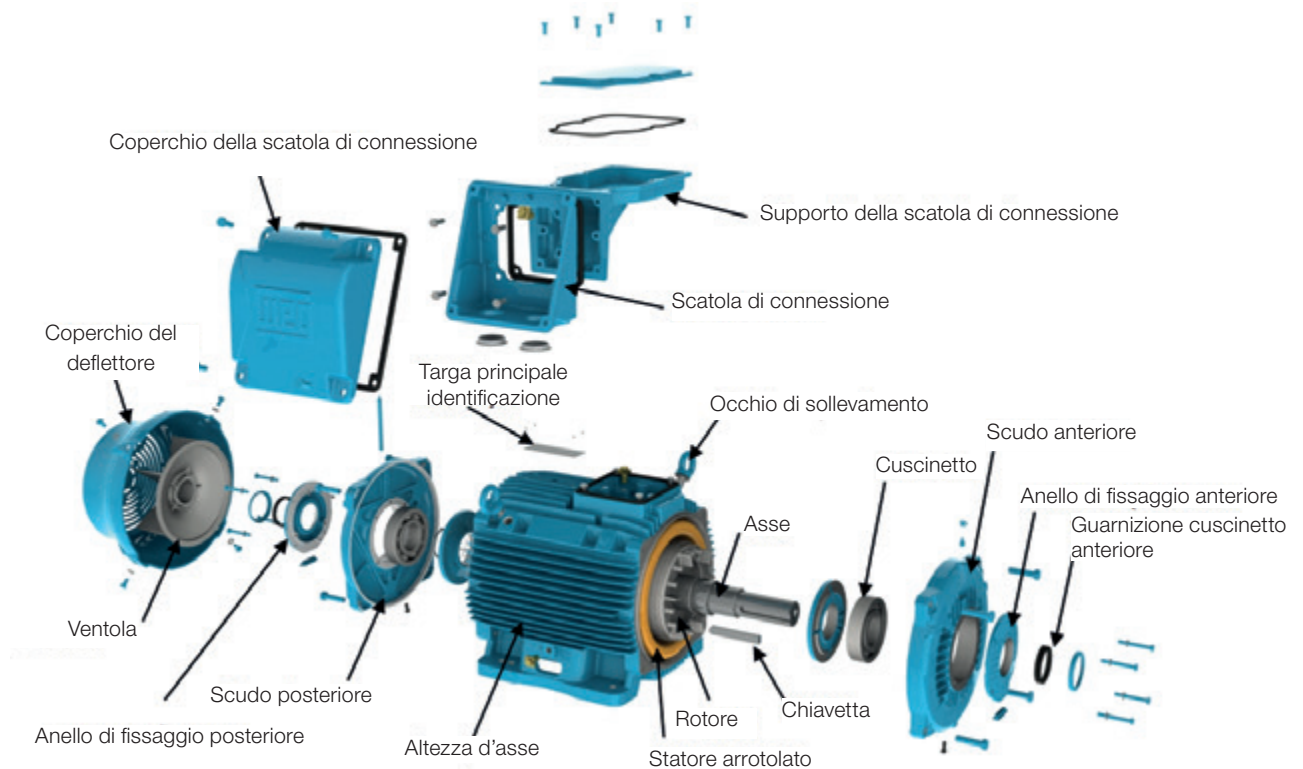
Vista disassemblata dei componenti di un motore W22
